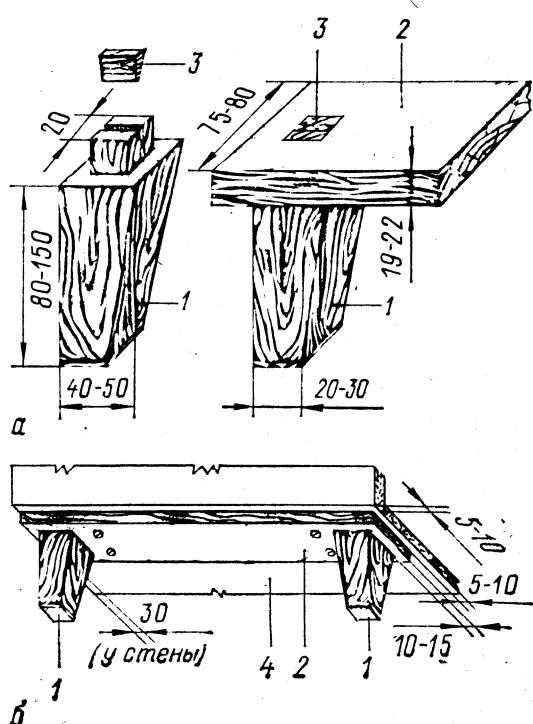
Ножки: а — соединение ножки с накладкой; б — крепление накладки к днищу; 1 — ножка; 2 — накладка; 3 — клин; 4 — днище
